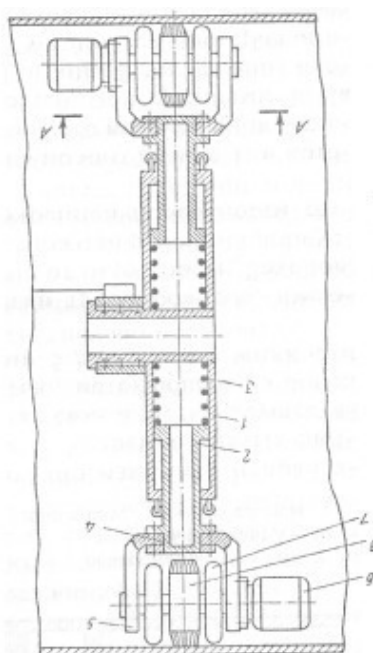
Рабочий орган очистного устройства для чистки внутренней поверхности трубопровода, имеющего отклонения по форме окружности, где 1 – водило; 2 – штанга; 3 – пружины; 4 – цилиндр; 5 – вилки; 6 – электродвигатель; 7 – приводное колесо; 8 – дисковая щетка.
